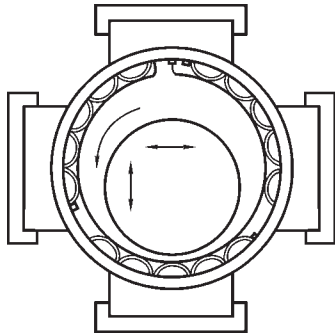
Конструкция магнитно-газодинамического подшипника [2]
